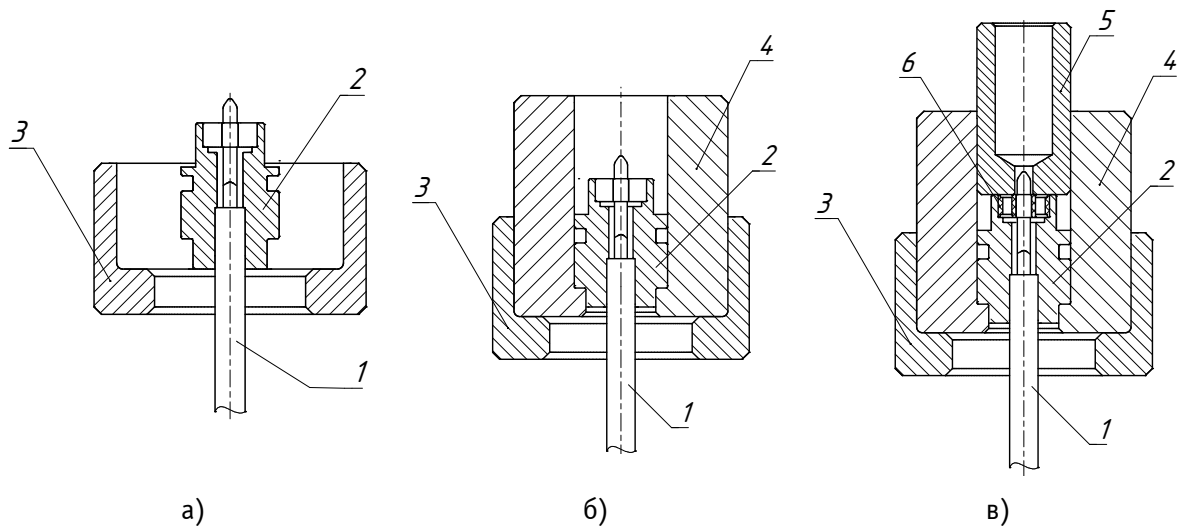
Приспособление для запрессовки диэлектрической опоры в кабельный соединитель ЖНКЮ.296361.014-01:
